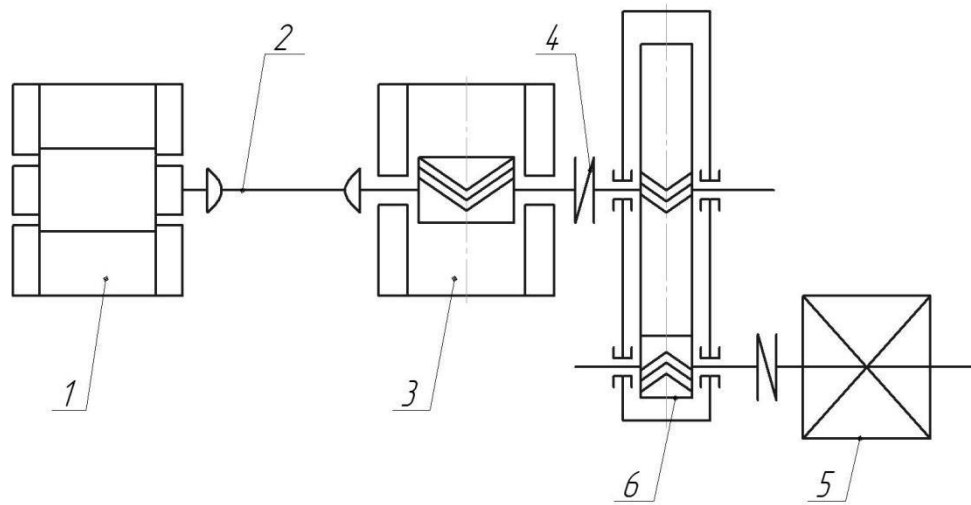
Схема розташування основного обладнання прокатного стану: 1 – робоча кліть; 2 – шпindel; 3 – муфта корінна; 4 – редуктор; 5 – муфта моторна; 6 – редуктор
